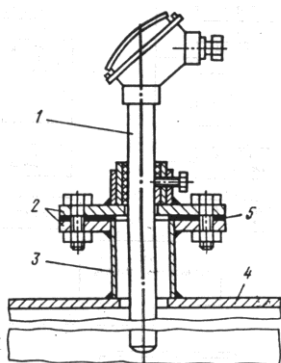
Схеми встановлення термопари на трубопроводі
